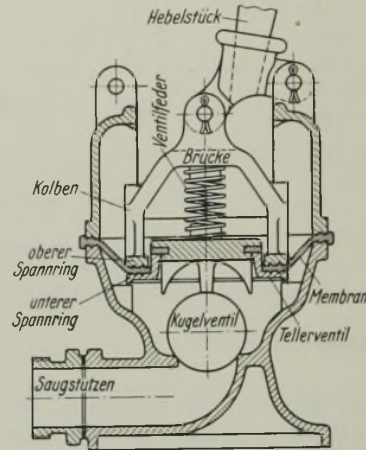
Saugpumpe für Schlammwasser mit federbelastetem Ventil im Kolben.
